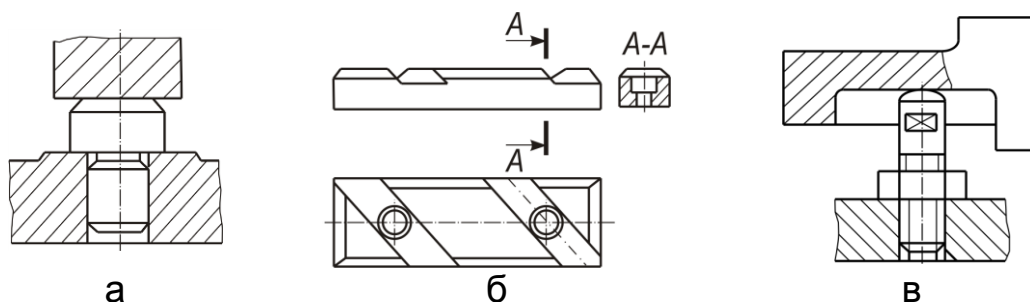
Встановлювальні елементи для призматичних заготовок
